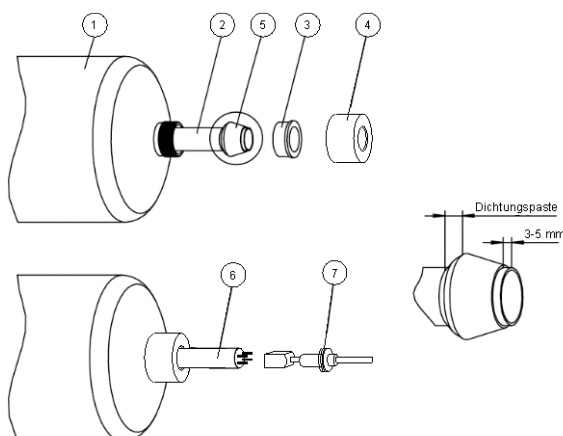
Сборочный чертёж UV 60 S – UV 200 S
